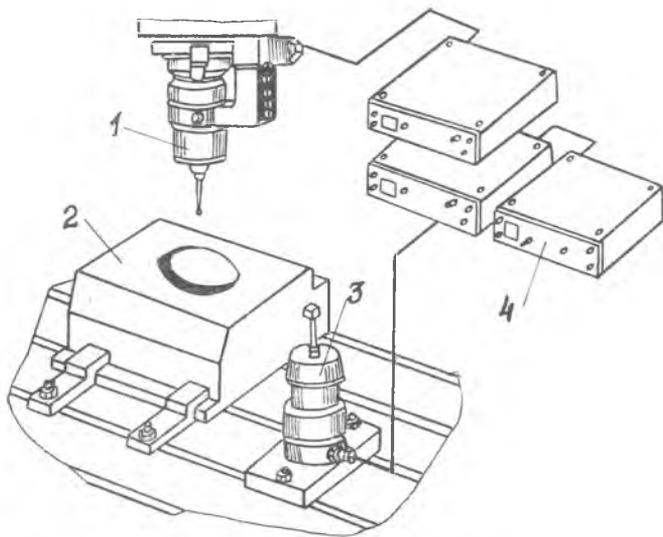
Схема установки измерительных шупов на станке с ЧПУ
